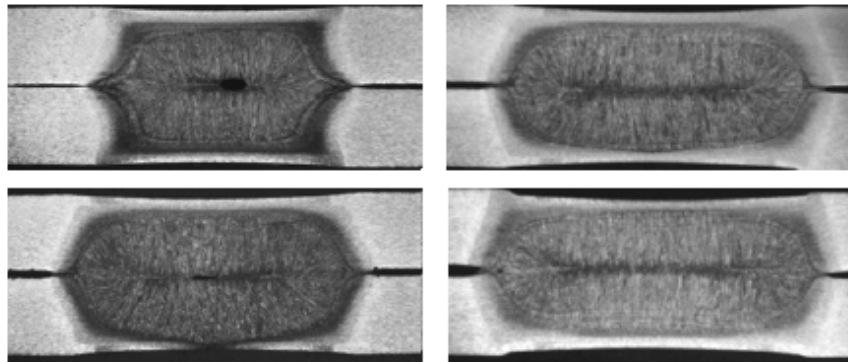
botões de solda feitos com diferentes eletrodos.
